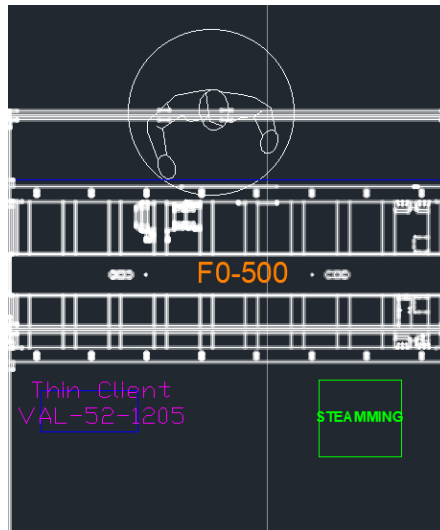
Puesto de montaje estación F0-500. (Fuente: Elaboración propia)
